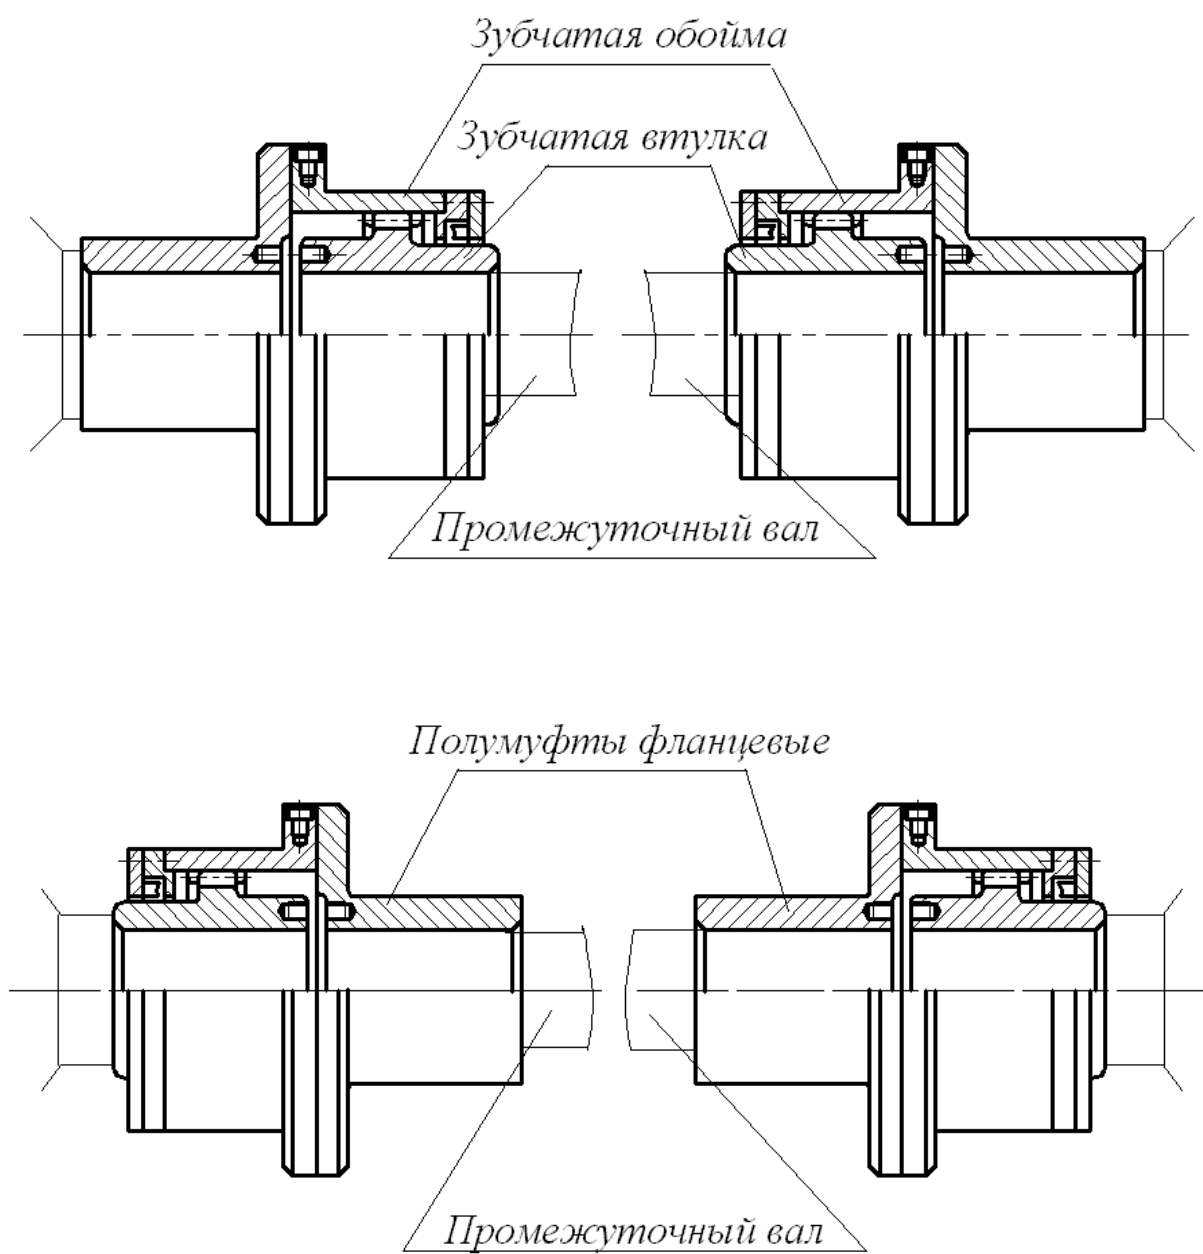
Варианты сборки зубчатых муфт типа 2 с промежуточными валами
